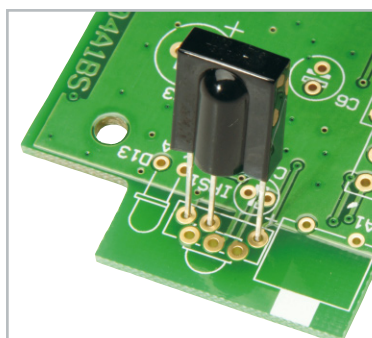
So erfolgt die richtige Bestückung des IR-Empfängers.
